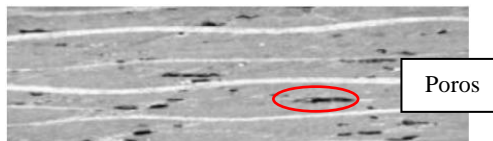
Defecto por porosidad uniformemente distribuida. Extraído de [29].
